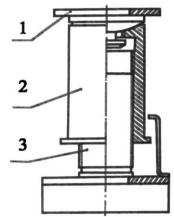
Устройство подрессорника 1 – пята; 2 – гайка; 3 – основание.
